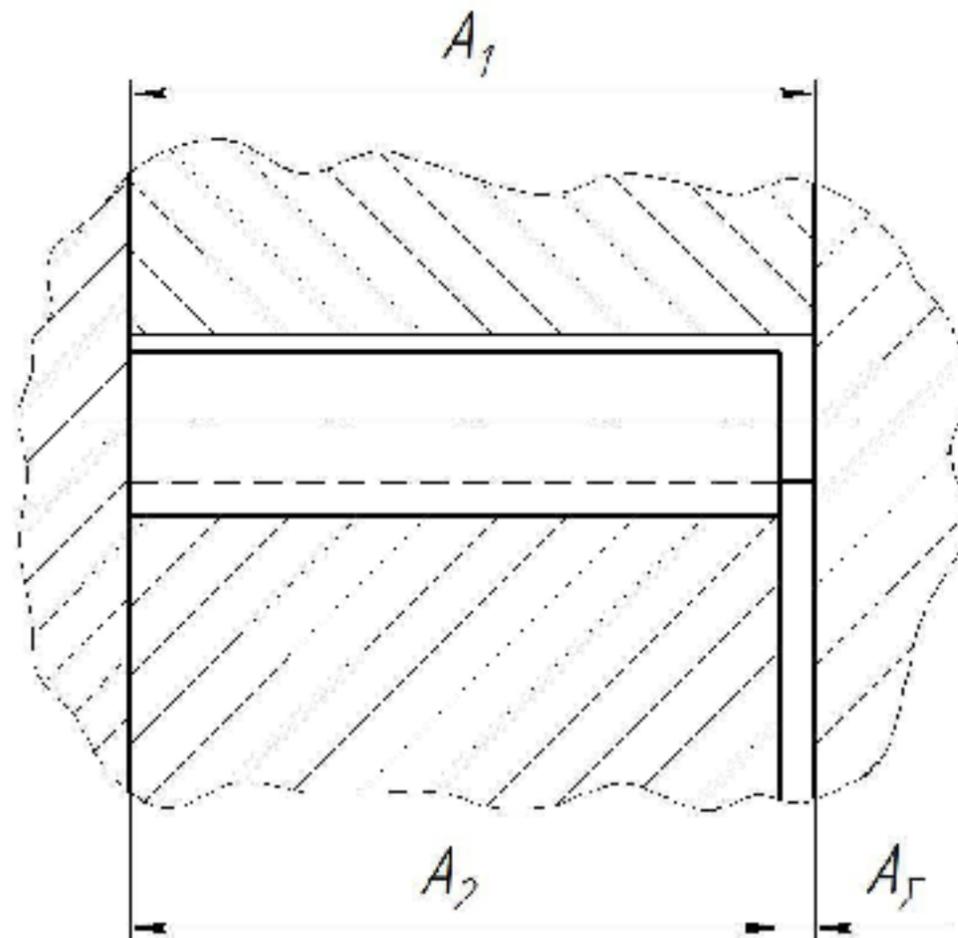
Схема розмірного ланцюга, що пов'язує розміри A_1 та A_2 ширин зубчастих вінців шестерень із зазором між торцем шестерні меншої ширини і компенсатором
